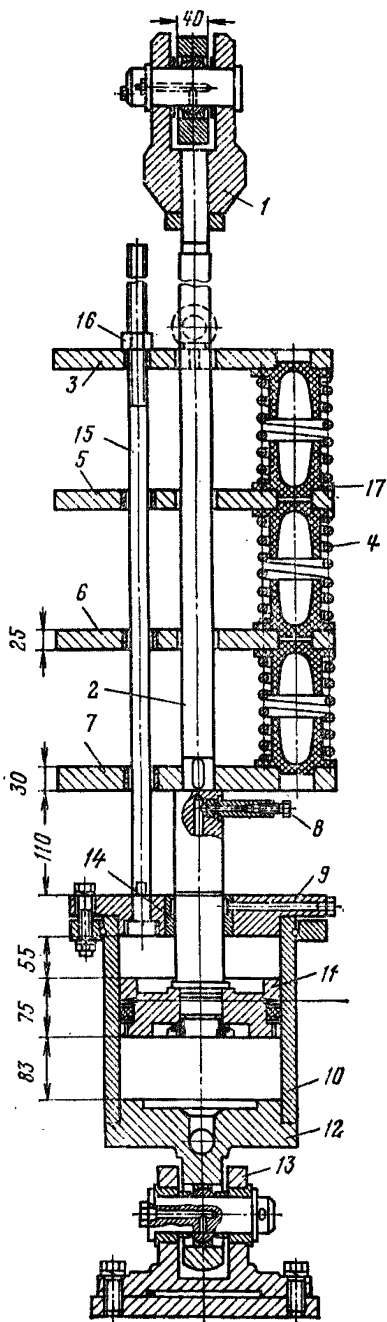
Пружинно-гидравлический привод тормоза подъемных машин Ц-2×1,5 и 2Ц-2×1,1: 1 — вилка; 2 — тяга; 3 — верхний диск; 4 — пружины; 5—6 — промежуточные диски; 7 — опорный диск; 8 — воздухоотводная пробка; 9 и 12 — верхняя и нижняя крышки; 10 — цилиндр; 11 — поршень; 13 — опора; 14 — бронзовая втулка; 15 — тяга; 16 — гайки; 17 — стакан
